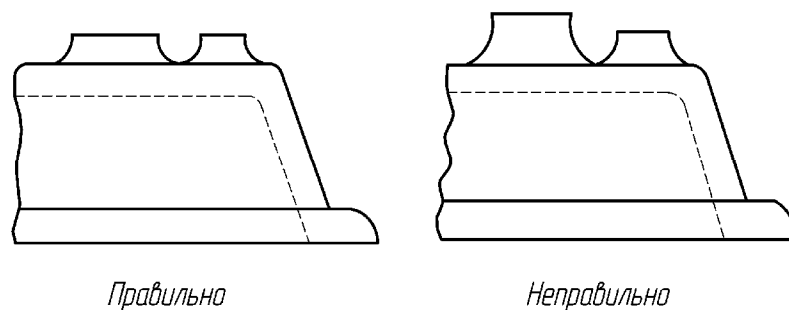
Конструирование бобышек и приливов с обрабатываемыми поверхностями
